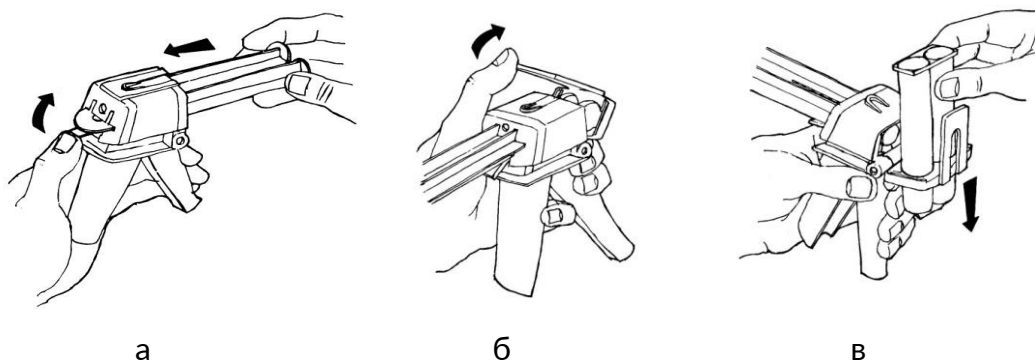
Сборка и подготовка к работе ручного дозатора.
